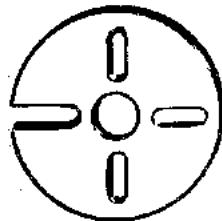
Plato de arrastre para torno (Sheldon Machine Co., Inc.)
